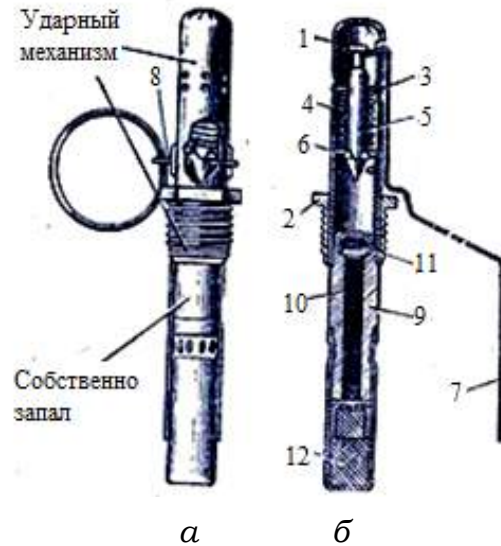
Запал гранаты УЗРГМ-2: а – общий вид; б – в разрезе; 1 – трубка ударного механизма; 2 – соединительная втулка; 3 – направляющая шайба; 4 – боевая пружина; 5 – ударник; 6 – шайба ударника; 7 – спусковой рычаг; 8 – предохранительная чека; 9 – втулка замедлителя; 10 – замедлитель; 11 – капсуля-детонатор; 12 – детонатор
